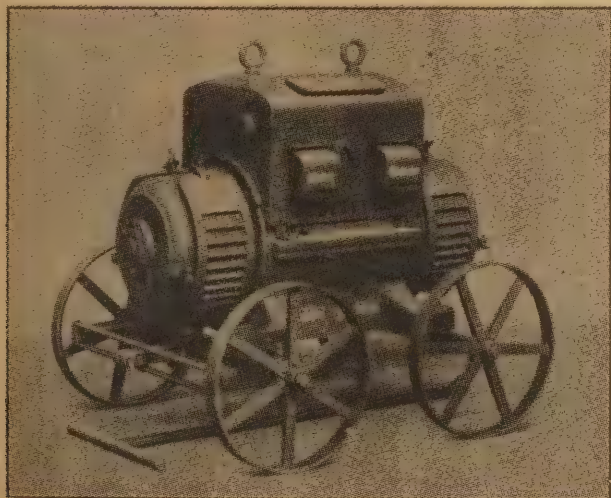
Fährbarer Schweißstrom-Erzeuger der Siemens-Schuckert-Werke.
